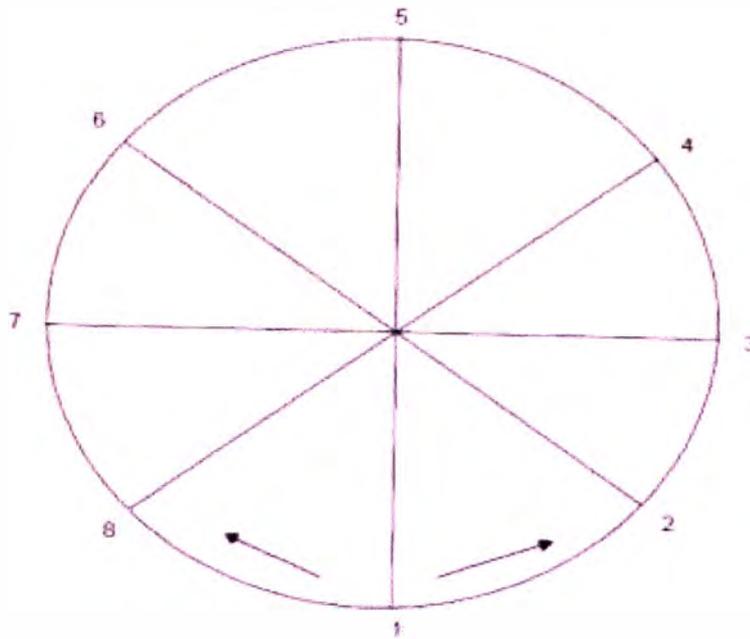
Posiciones y tramos a soldar (Vista de soldeo entre tramos 1-8 y 1-2)
